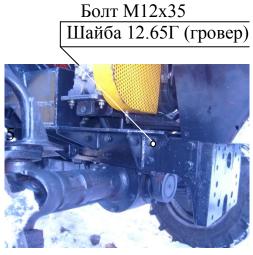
Основные узлы Оборудования. Порядок сборки и установки на базовый трактор.
